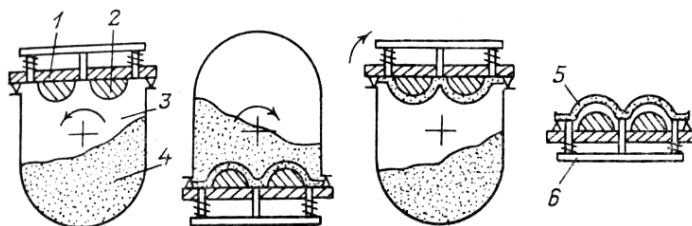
Схема виготовлення оболонкових напівформ
